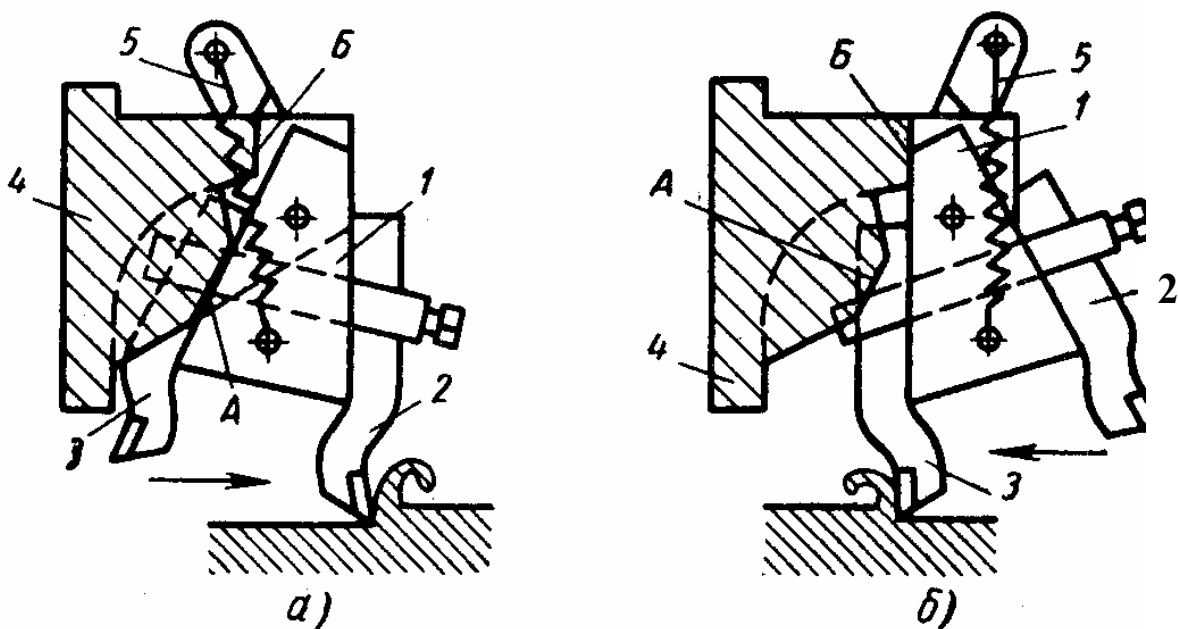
Схеми роботи двосторонньої різцевої головки: а – прямий хід; б – зворотний хід; 1 – різцетримач; 2, 3 – різці прямого і зворотного ходів; 4 – корпус головки; 5 - пружина
